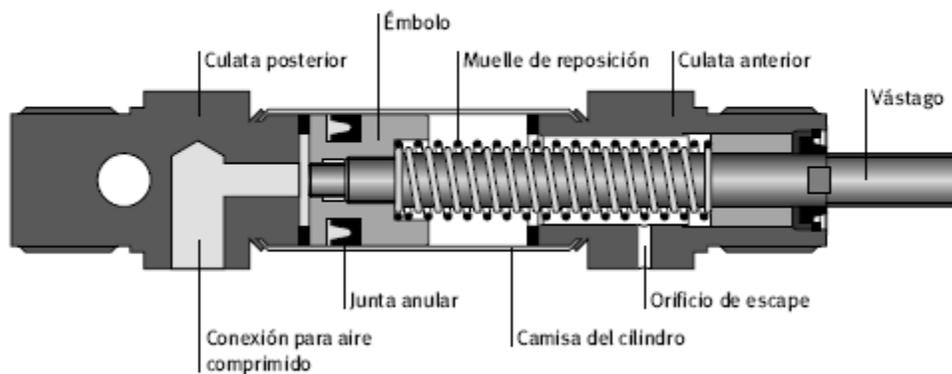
Partes principales de un Cilindro simple efecto. [26]
